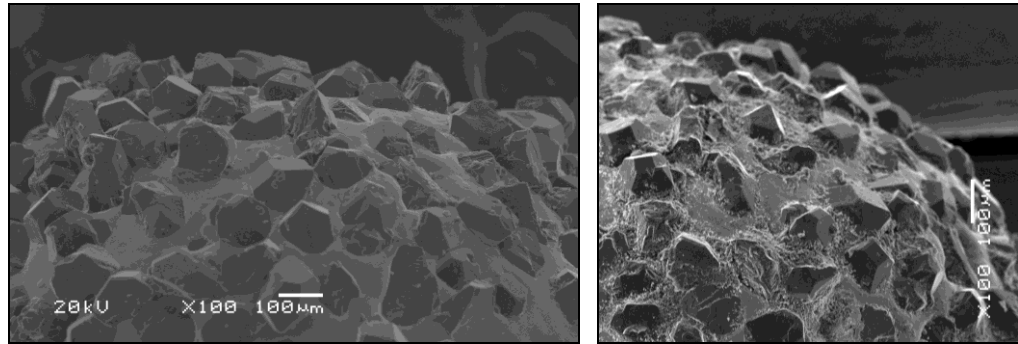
Em (A), fresa PMG\_720 antes da usinagem e em (B) após a usinagem, não demonstrando desgaste visível.
